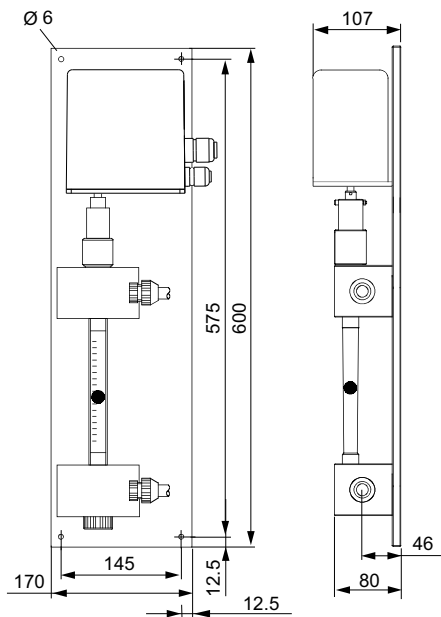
Dosierregler VGA-117 mit und ohne Stellmotor
